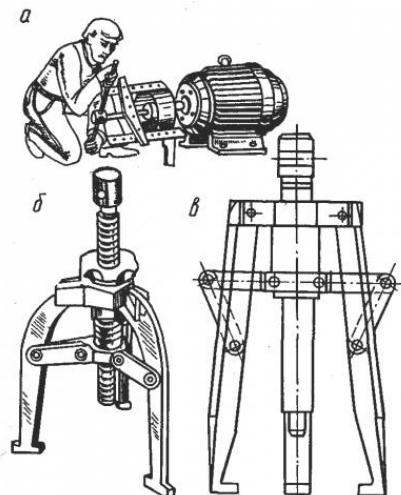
Снятие шкива с вала электродвигателя:
